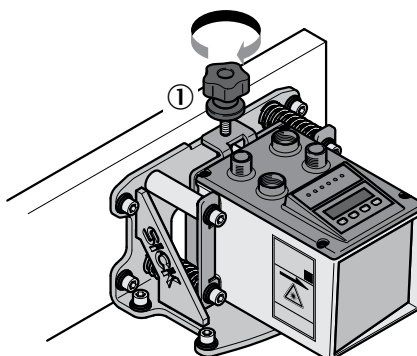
Entfernungs-Messgerät mit Rändelschraube befestigen
